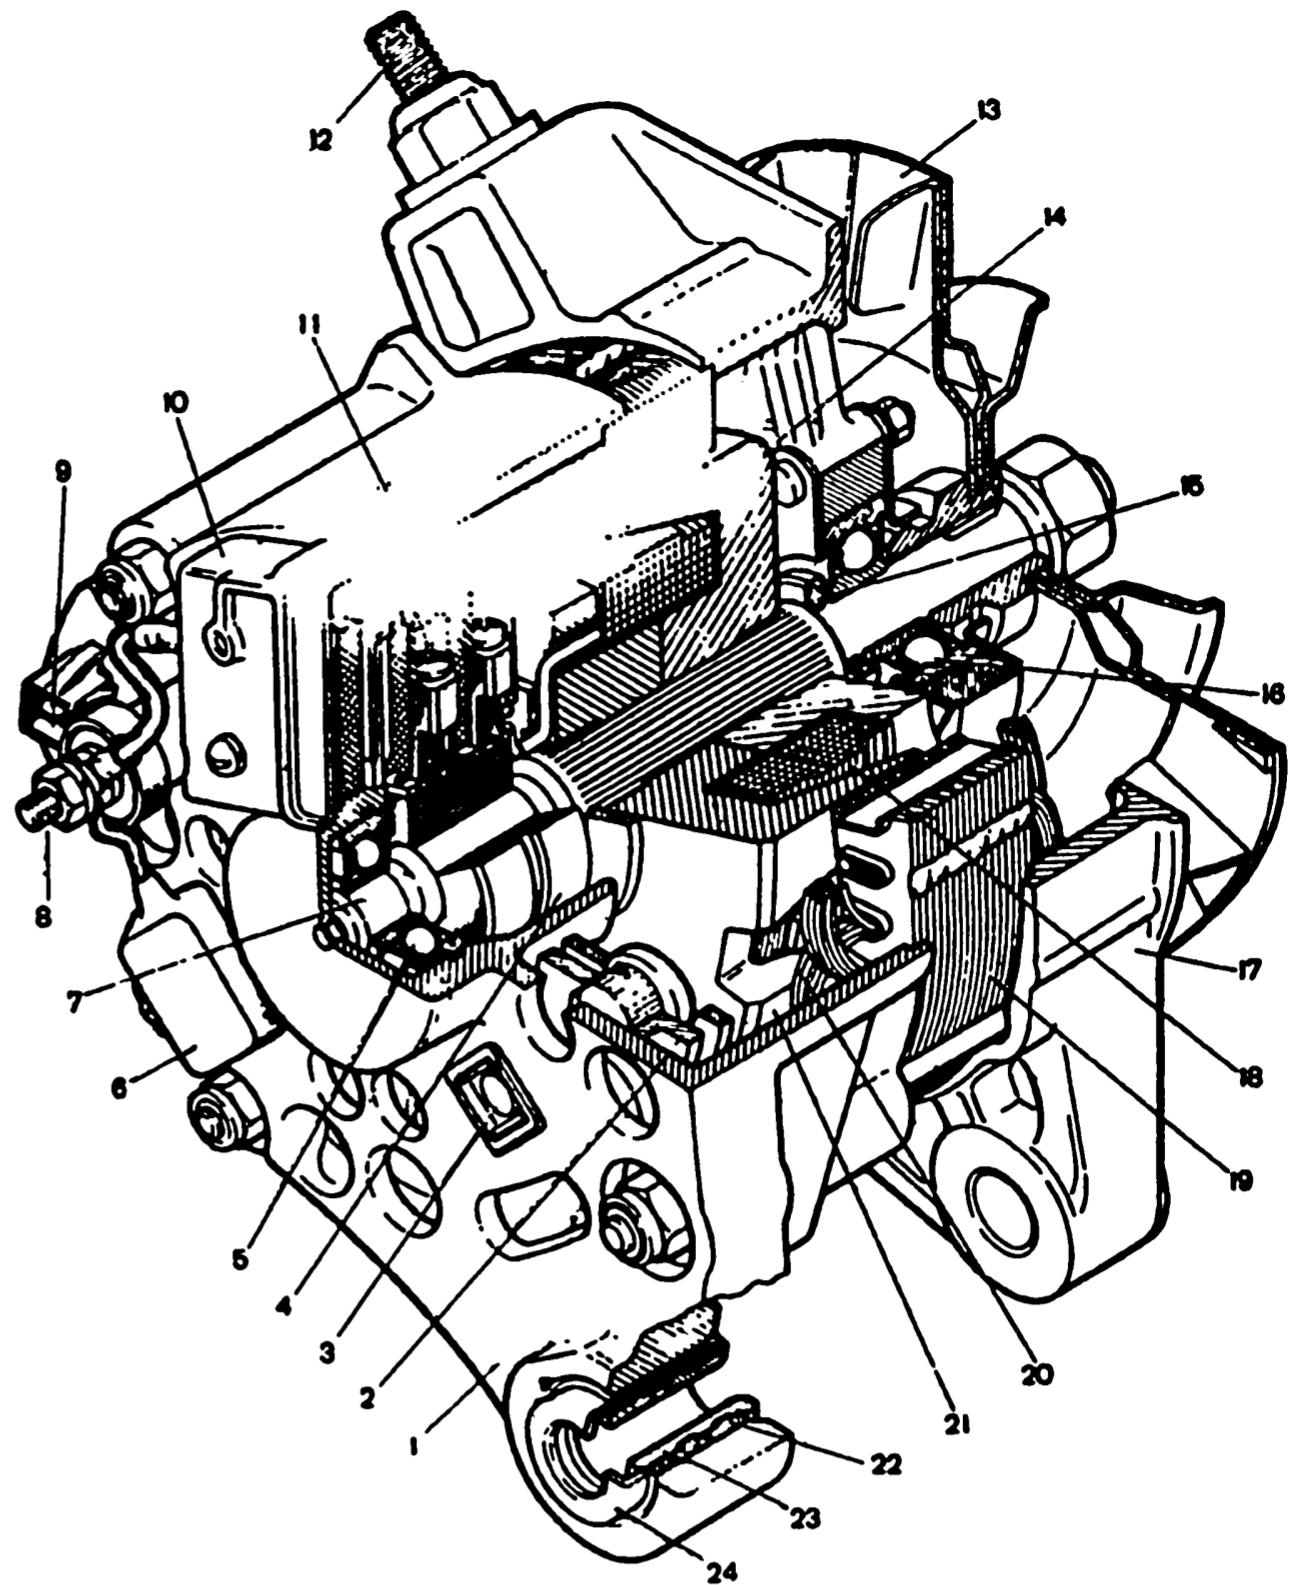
Генератор Г-222: 1 - крышка со стороны контактных колец; 2 - выпрямительный блок; 3 - винт крепления выпрямительного блока; 4 - контактное кольцо; 5 - задний шарикоподшипник; 6 - конденсатор; 7 - вал ротора; 8 - вывод «30» генератора; 9 - штекер нулевого провода; 10 - регулятор напряжения со щеткодержателем; 11 - щетка; 12 - шпилька крепления генератора к натяжной планке; 13 - шкив с вентилятором; 14 - полюсный наконечник ротора; 15 - втулка; 16 - передний шарикоподшипник; 17 - крышка со стороны привода; 18 - обмотка ротора; 19 - статор; 20 - обмотка статора; 21 - полюсный наконечник ротора; 22 - буферная втулка; 23 - втулка; 24 - поджимная втулка
